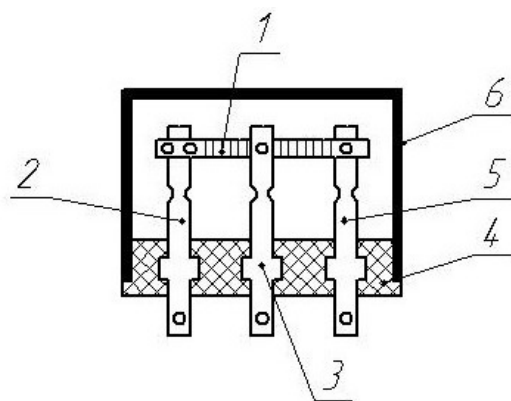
Реле-прерыватель РС-492: 1 – биметаллическая пластина; 2, 3, 5 – стойки-штекеры; 4 – пластмассовое основание; 6 – колпачок-крышка
